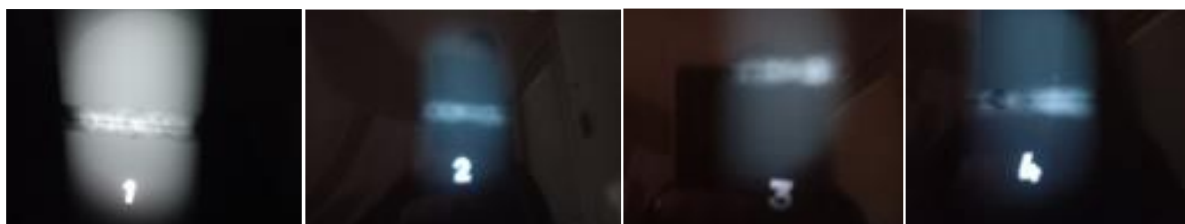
Inclusions de laitier dans les quatre éprouvettes soudées
